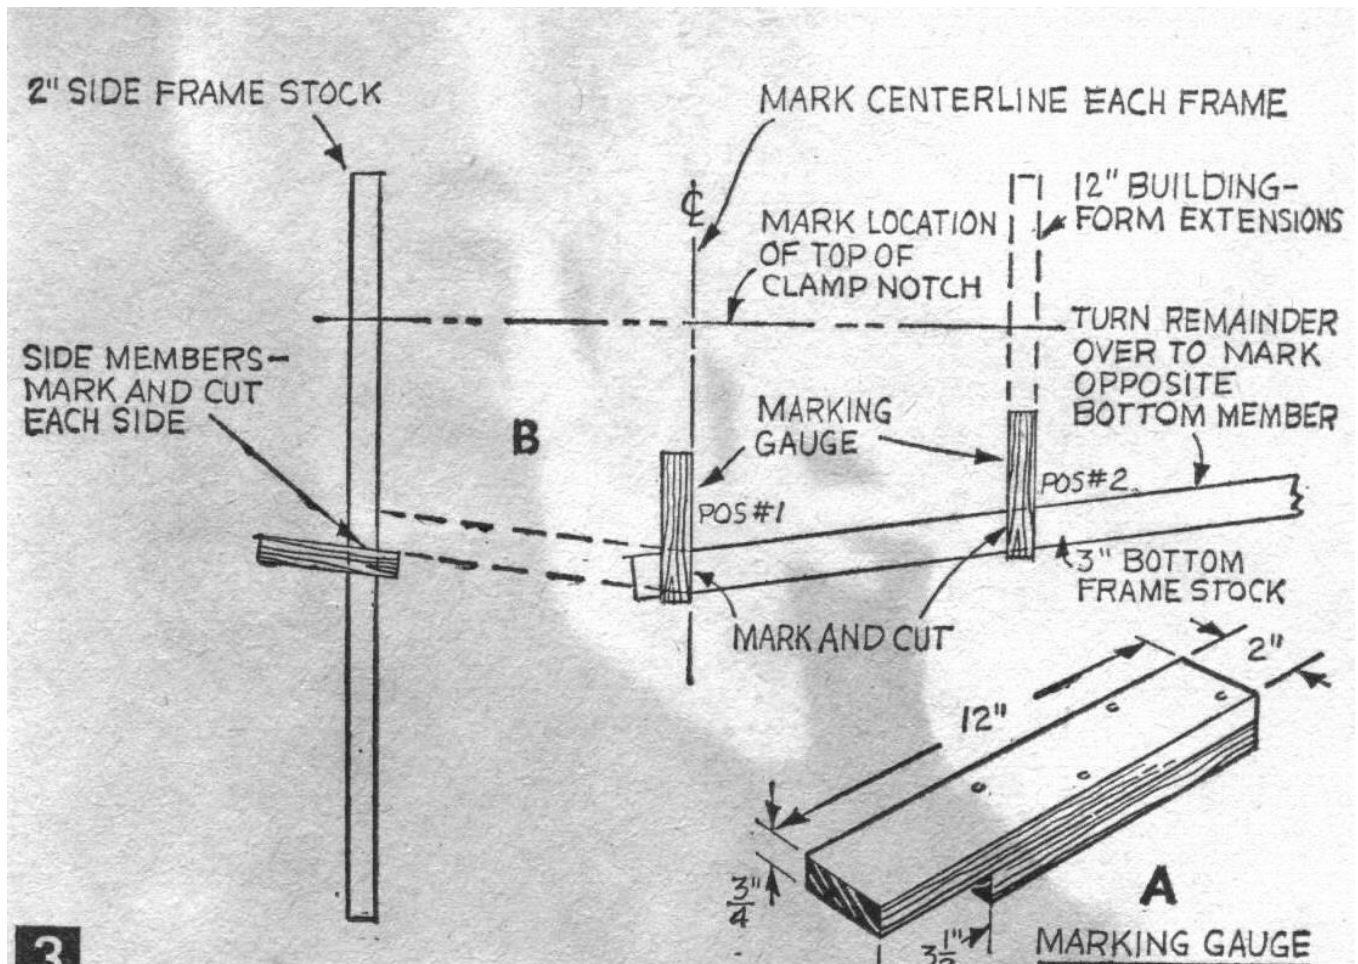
Vista plano cuaderna típica modelo original (Fuente: Svenson.com)
